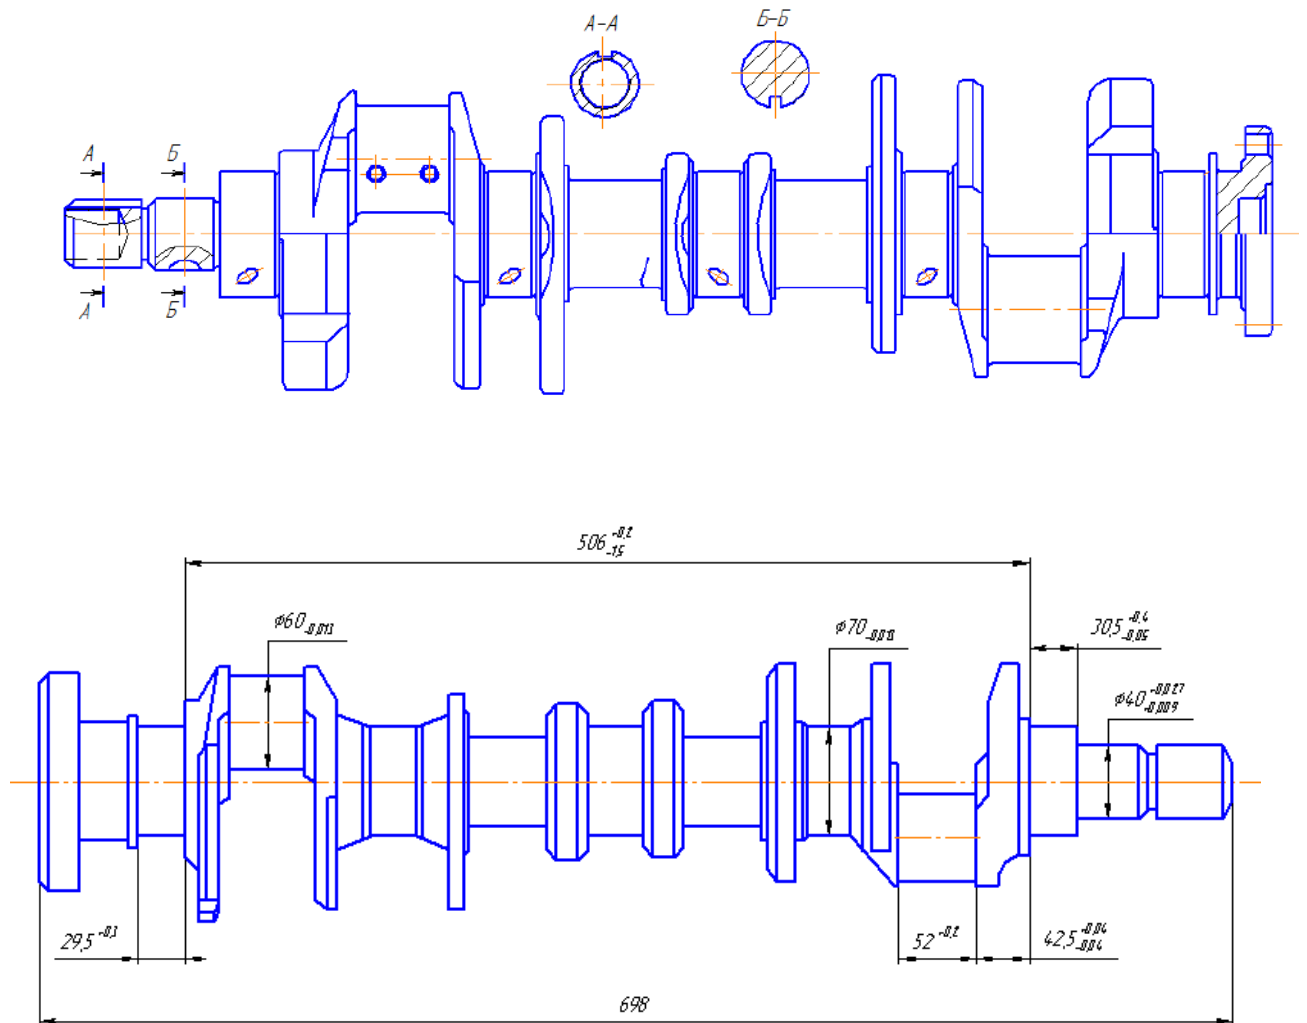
Колінчастий вал двигуна 3МЗ-511.1000402 Євро-0
